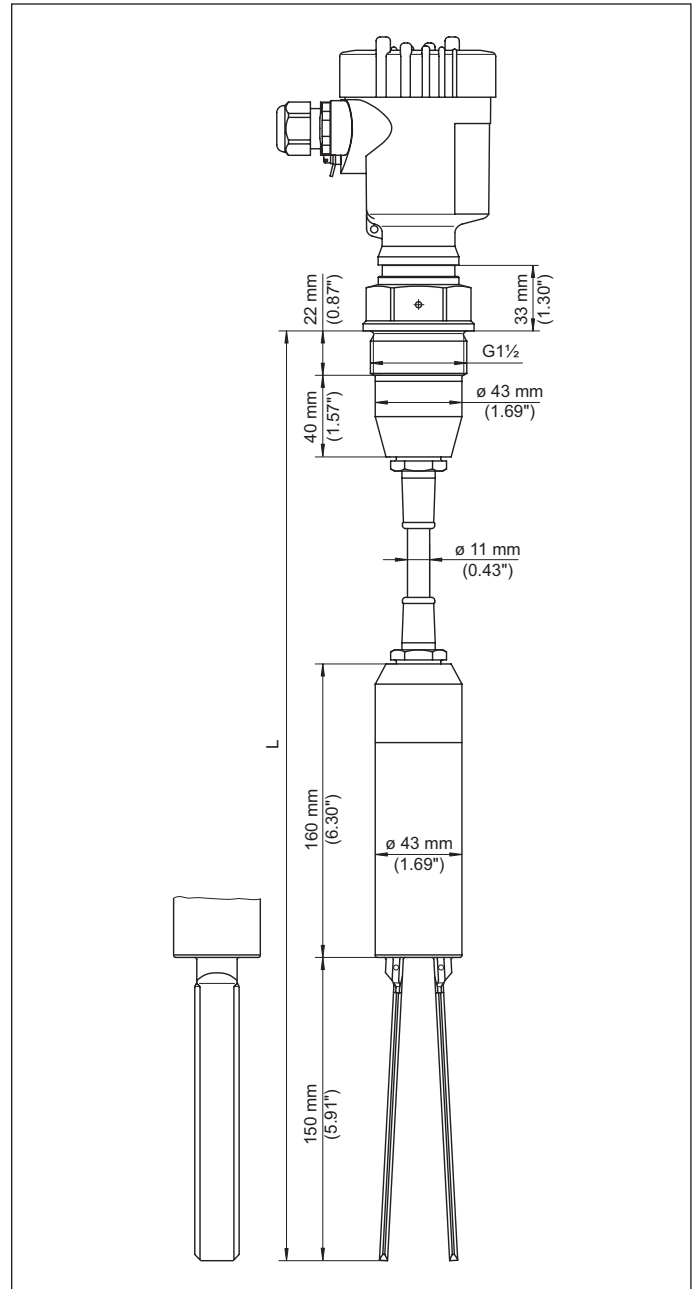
VEGAWAVE 62 - Gewindeausführung G1½
